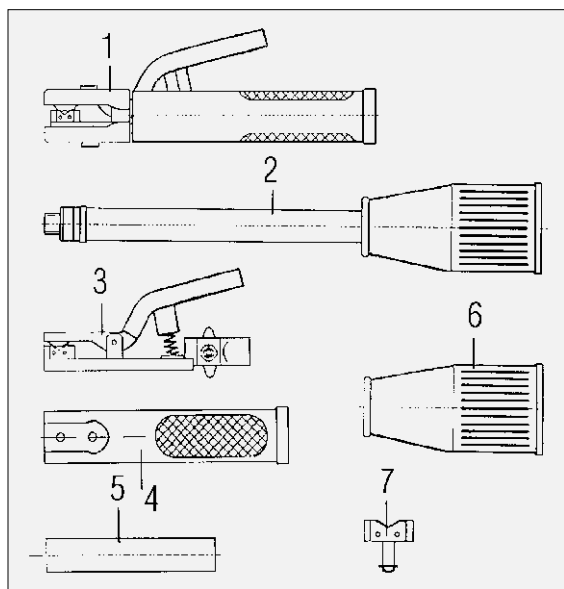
Основные узлы ручного резака для воздушно-дуговой строжки
